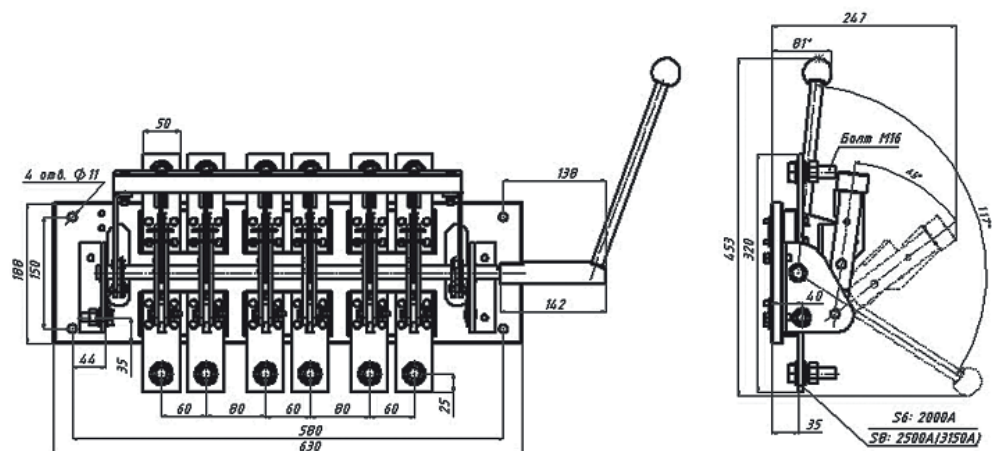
Разъединитель РЕ19 на два направления с рычагом для полюсного оперирования штангой
